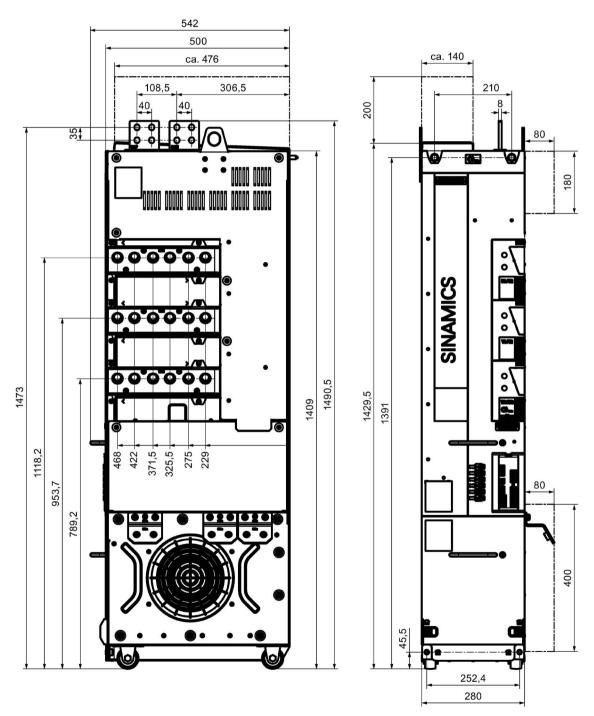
Габаритный чертеж модуля двигателя формата «шасси-2», типоразмер FS4. Вид сбоку, вид спереди
